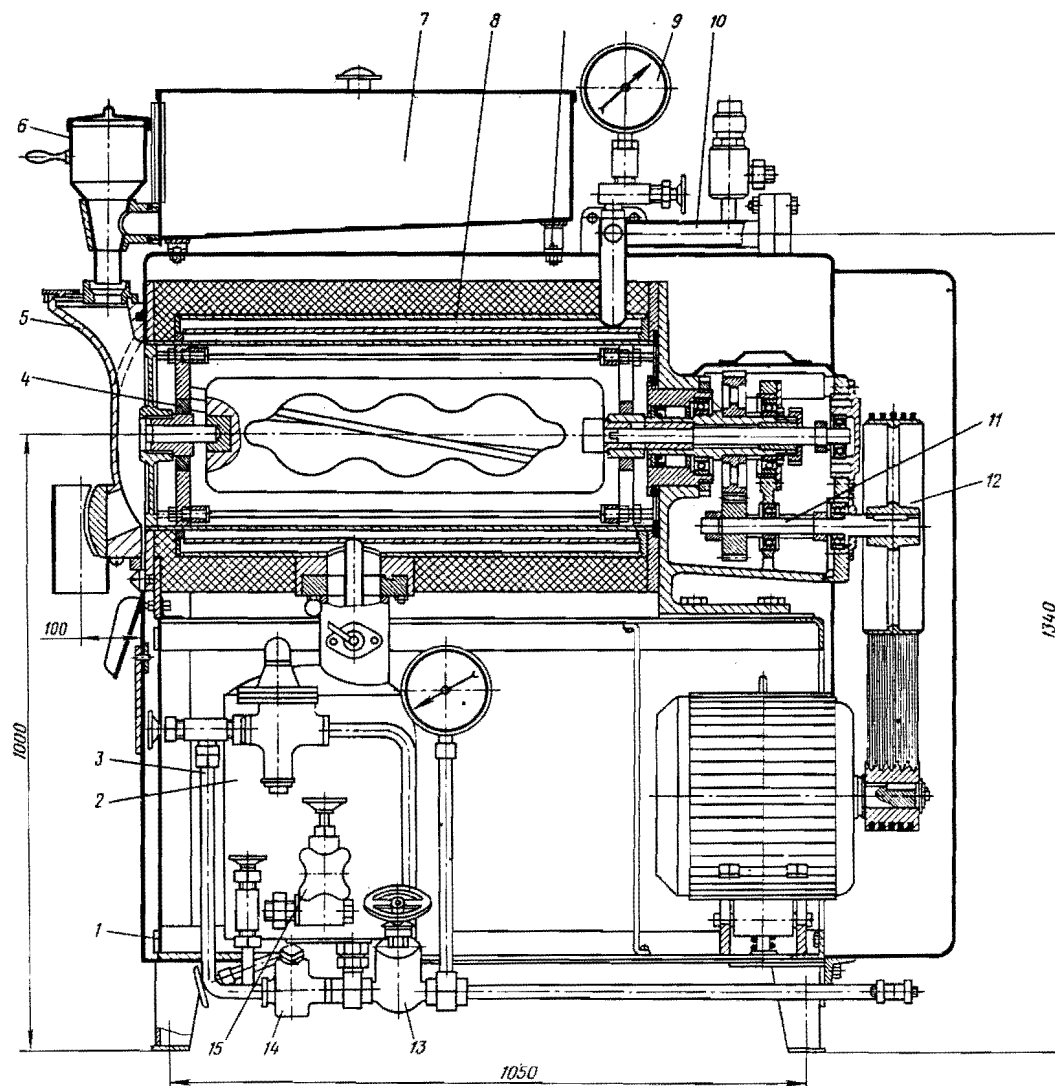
Общий вид (разрез) фризера марки ФФА-М для мороженого:
